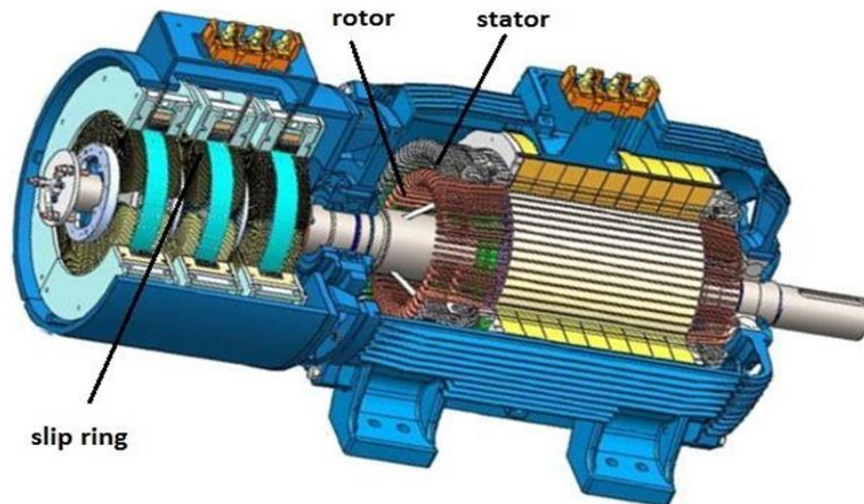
COUPPE D'UN GENERATEUR A INDUCTION A ROTOR BOBINE [36].
